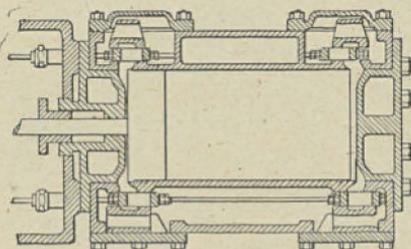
Coupe horizontale de la valve Porter Allen.
